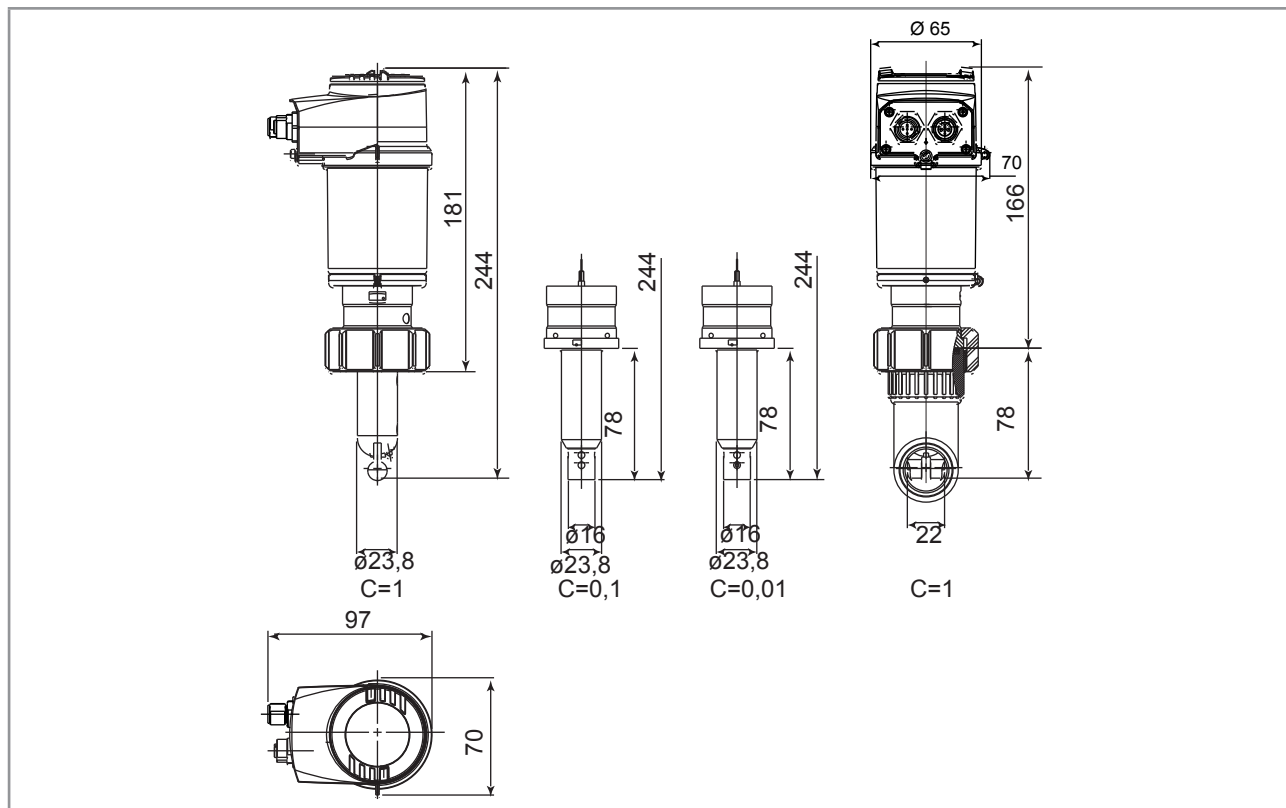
Габаритные размеры преобразователя 8222 [мм]
